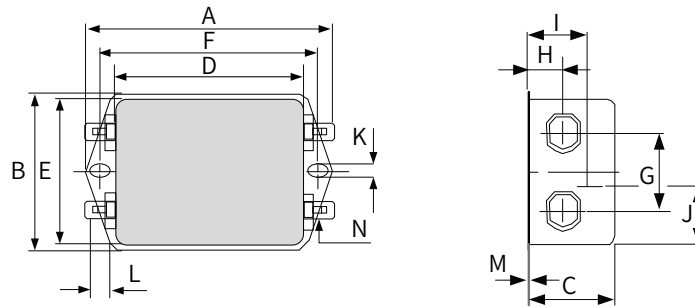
Габаритный чертеж фильтров серии FN 2090 (ед. изм.: мм)
